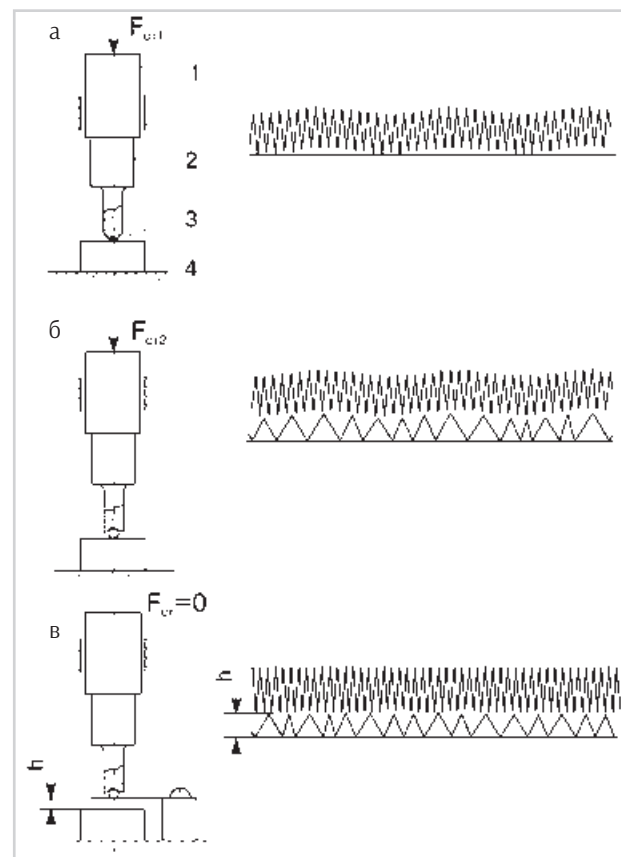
Схемы выполнения ВМП металлов: а — жесткое закрепление деформирующего элемента статическим усилием $F_{ст1}$ (1 — излучатель; 2 — концентратор; 3 — деформирующий элемент; 4 — обрабатываемая деталь); б — с поджатием акустической системы усилием $F_{ст2}$ и пассивным деформирующим элементом; в — с колебаниями деформирующего элемента в заданном малом зазоре h (Кныш В. В., Кузьменко А. З.). Повышение сопротивления усталости сварных соединений высокочастотной механической проковкой // Сварщик. — 2005. — № 2. — С. 19–21)
